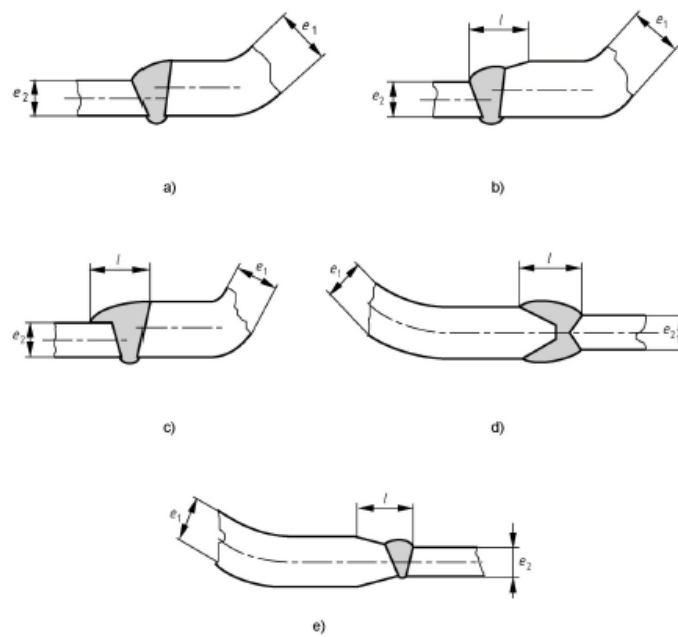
Soldadura entre envolvente y fondo
